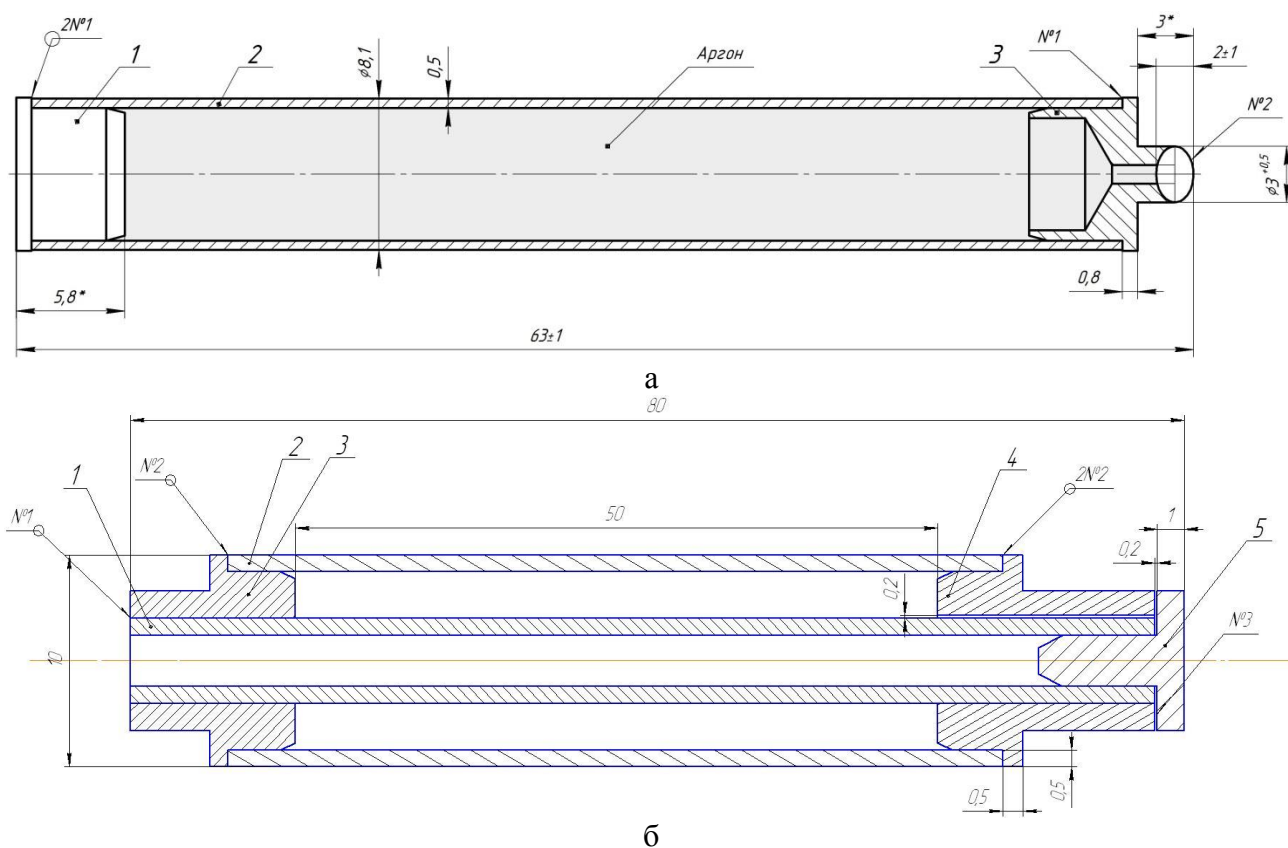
Схема трубчатых газонаполненных образцов, состоящих из одной трубки и концевых деталей (а): нижняя заглушка (1), внешний трубчатый элемент (2), технологическая заглушка (3) и двух коаксиальных трубок (б): внутренний трубчатый элемент (1), внешний трубчатый элемент (2), нижняя (3) и верхняя (4) кольцевые пробки, технологическая заглушка (5)
